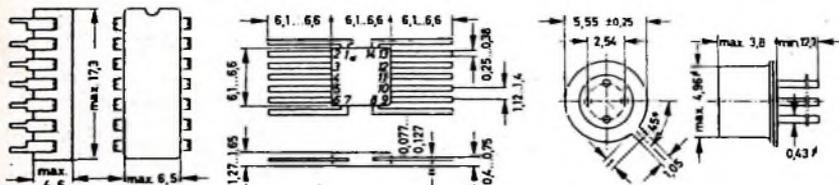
Verschiedene Gehäuseformen für integrierte Schaltkreise; a) D-1-Gehäuse, b) „flat-pack“, c) TO-5-Gehäuse
